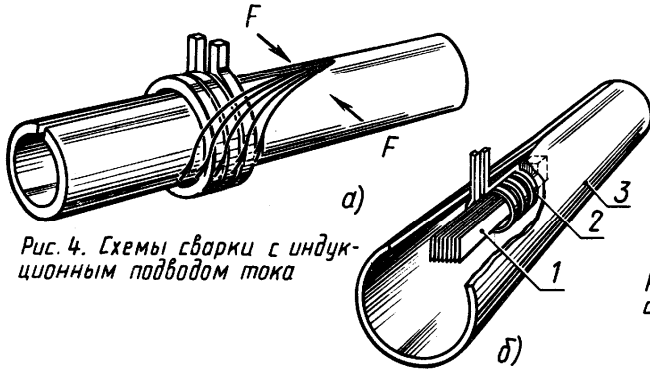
Схемы сварки с индукционным подводом тока
